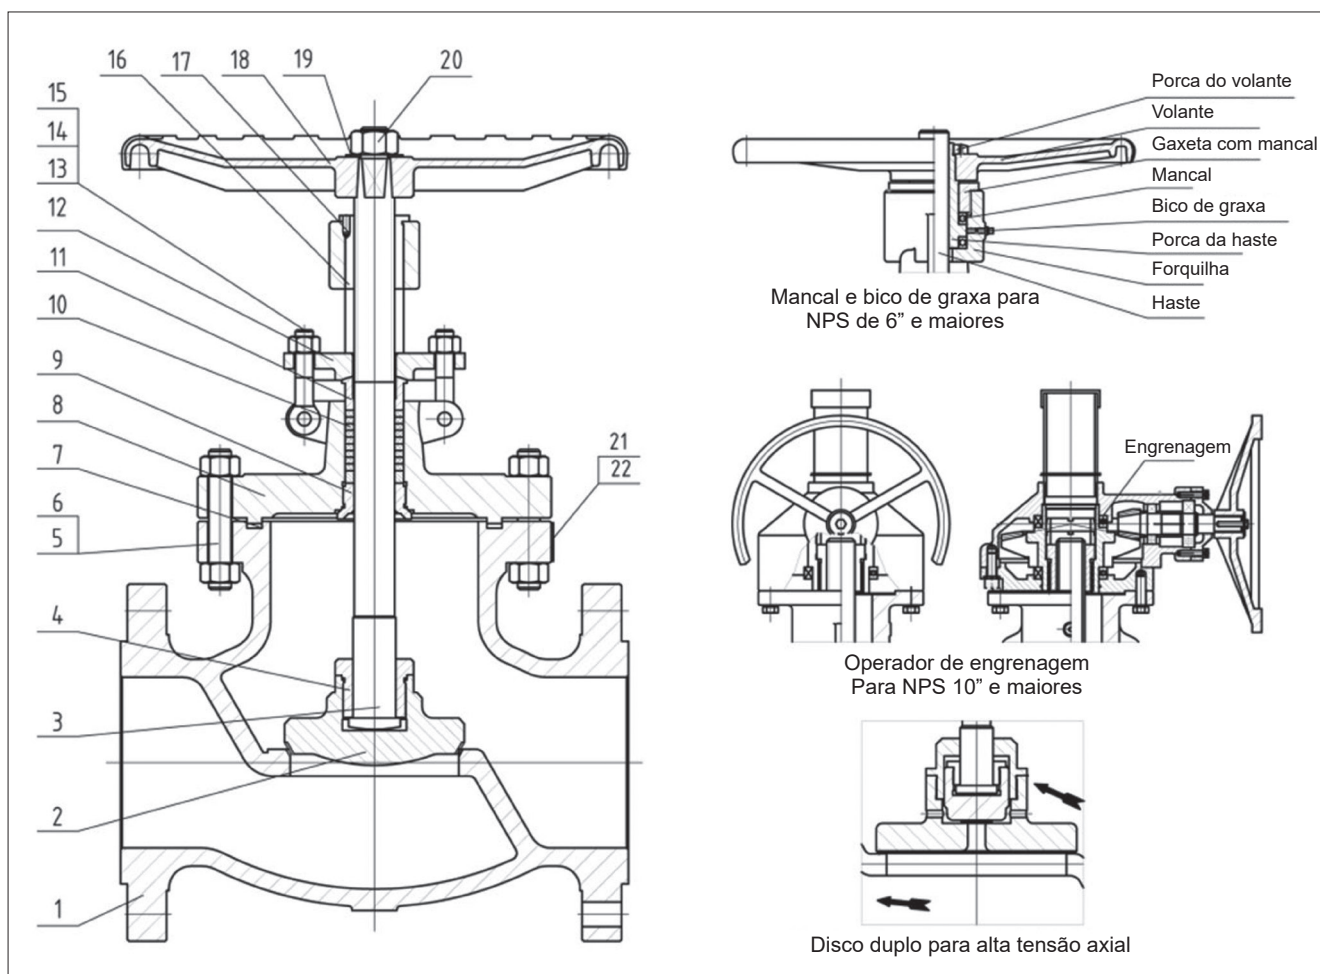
Válvula globo de aço fundido com tampa de parafuso
